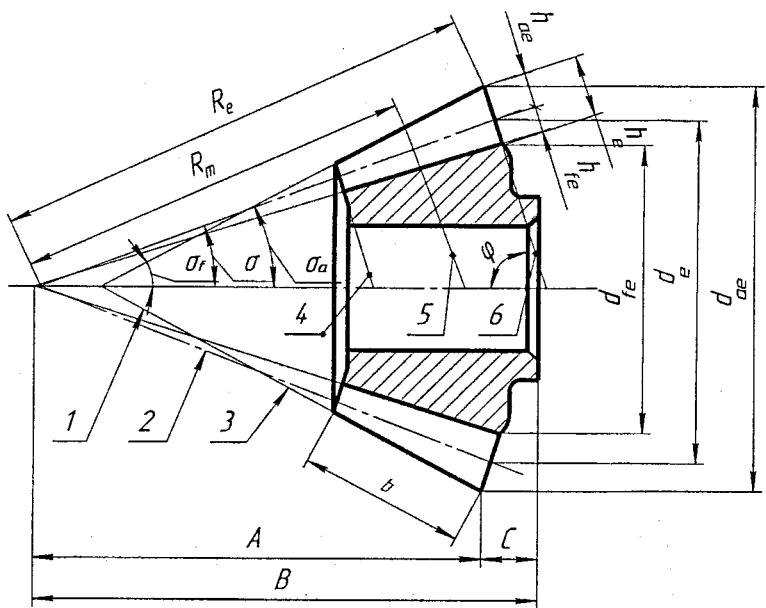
Елементи (*components*) конічного зубчастого колеса
